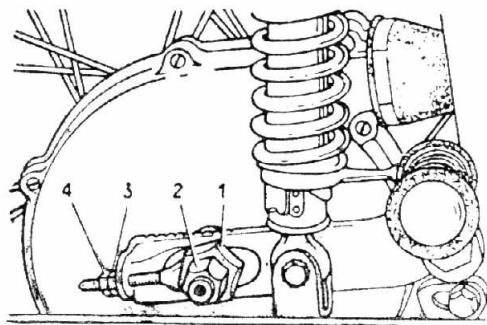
Регулировка натяжения цепи привода заднего колеса:
